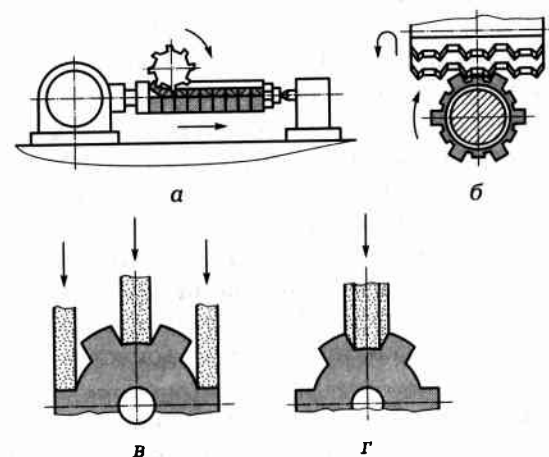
Схемы обработки шлицевых поверхностей на горизонтально-фрезерных (а), шлицефрезерных (б), плоскошлифовальных (в) и шлицешлифовальных (г) станках
